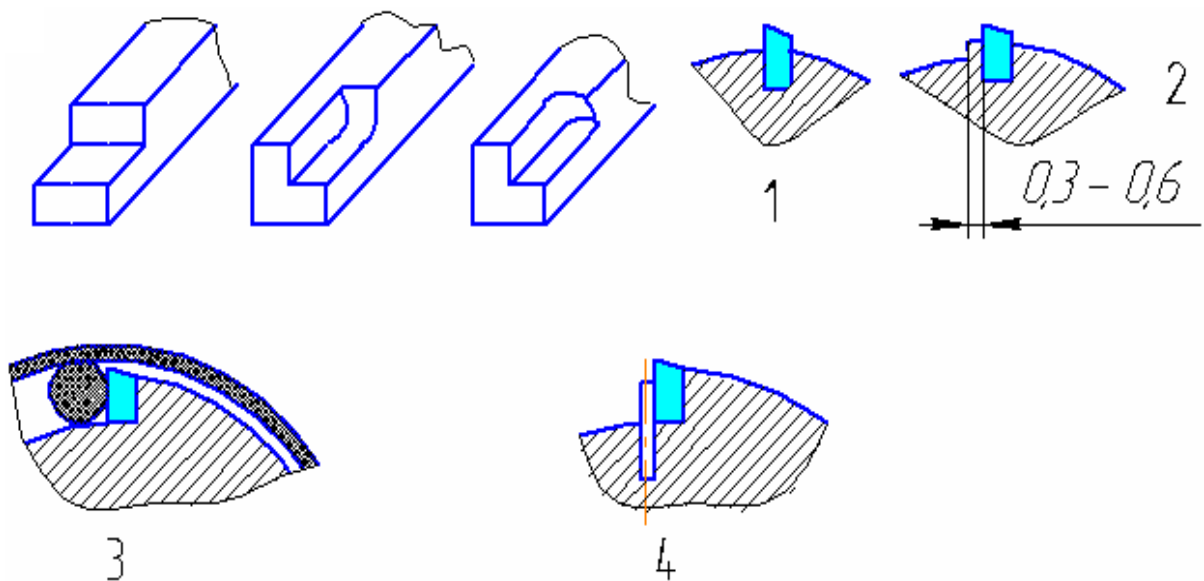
Форми пазів під пластини та засоби фіксування пластин перед припаюванням
